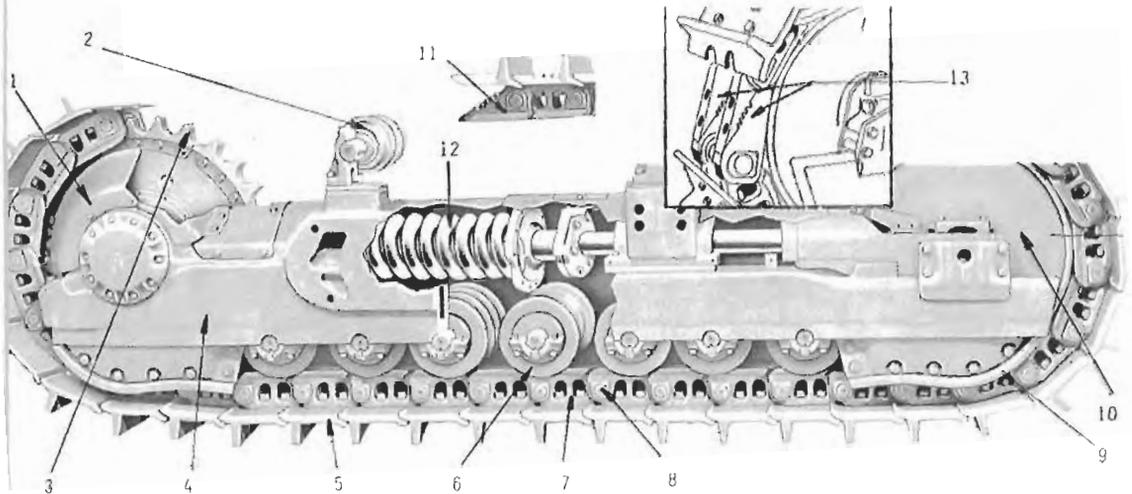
Carro completo seccionado (CAI). 1.- Protector de rueda motriz. 2.- Rodillo de apoyo superior. 3.- Segmentos atornillables de la rueda motriz. 4.- Larguero o bastidor. 5.- Zapata o teja. 6.- Rodillo de apoyo inferior. 7.- Eslabones de cadena. 8.- Bultones. 9.- Protector de rueda guía. 10.- Rueda guía. 11.- Eslabón de empalme de la cadena. 12.- Muelle de tensión y amortiguación. 13.- Detalle del eslabón de empalme.
